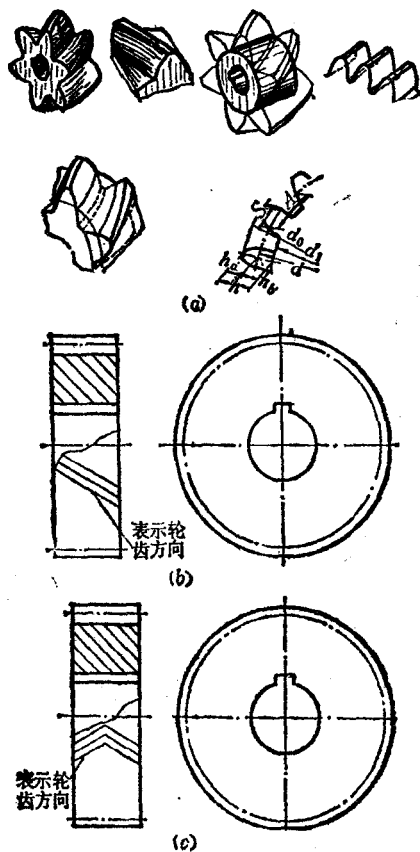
圆柱斜齿轮的立体图及圆柱齿斜轮、人字齿轮的画法
